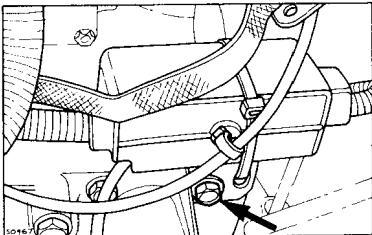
Болт крепления контактной коробки (отмечен стрелкой)
